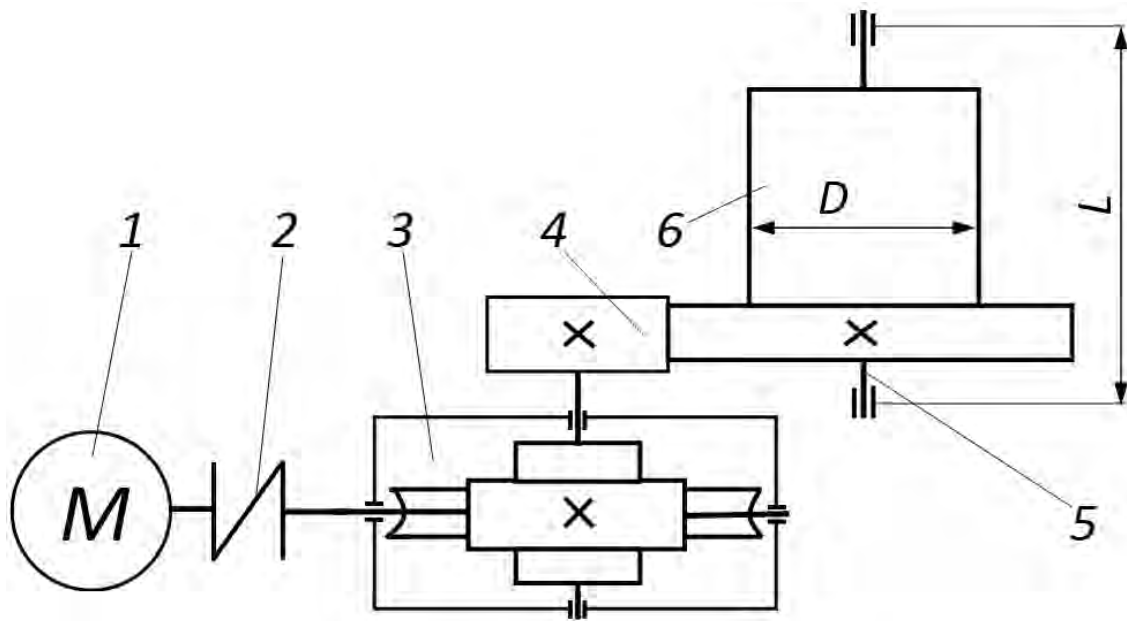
Схема привода лебедки подъема стрелы (вид сверху): 1 – асинхронный электродвигатель; 2 – муфта упругая втулочно-пальцевая; 3 – редуктор червячный с верхним расположением червяка; 4 – открытая цилиндрическая прямозубая передача; 5 – приводной вал; 6 – барабан с зубчатым колесом со встроенным устройством предохранения от перегрузок (с предохранительной муфтой по вращающему моменту)
